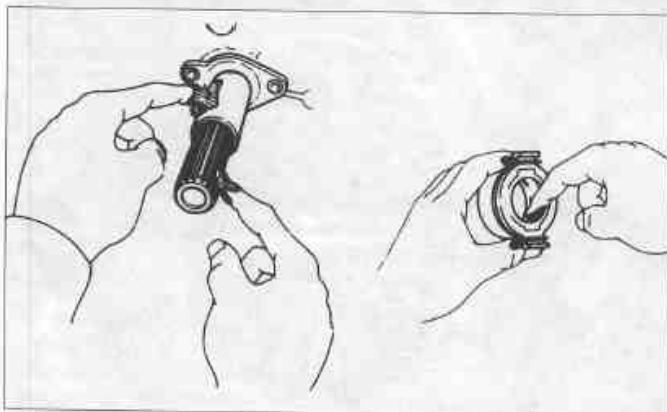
Нанесите тонкий слой смазки для сцепления на направляющую подшипника в коробке передач, а также заполните канавку подшипника выключения сцепления
